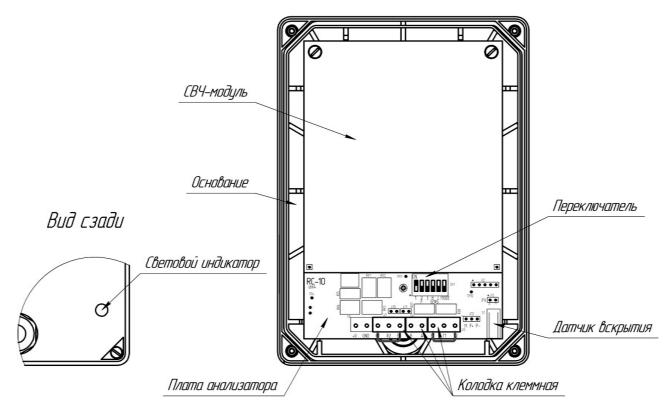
Внешний вид блока ПРМ со снятой крышкой
